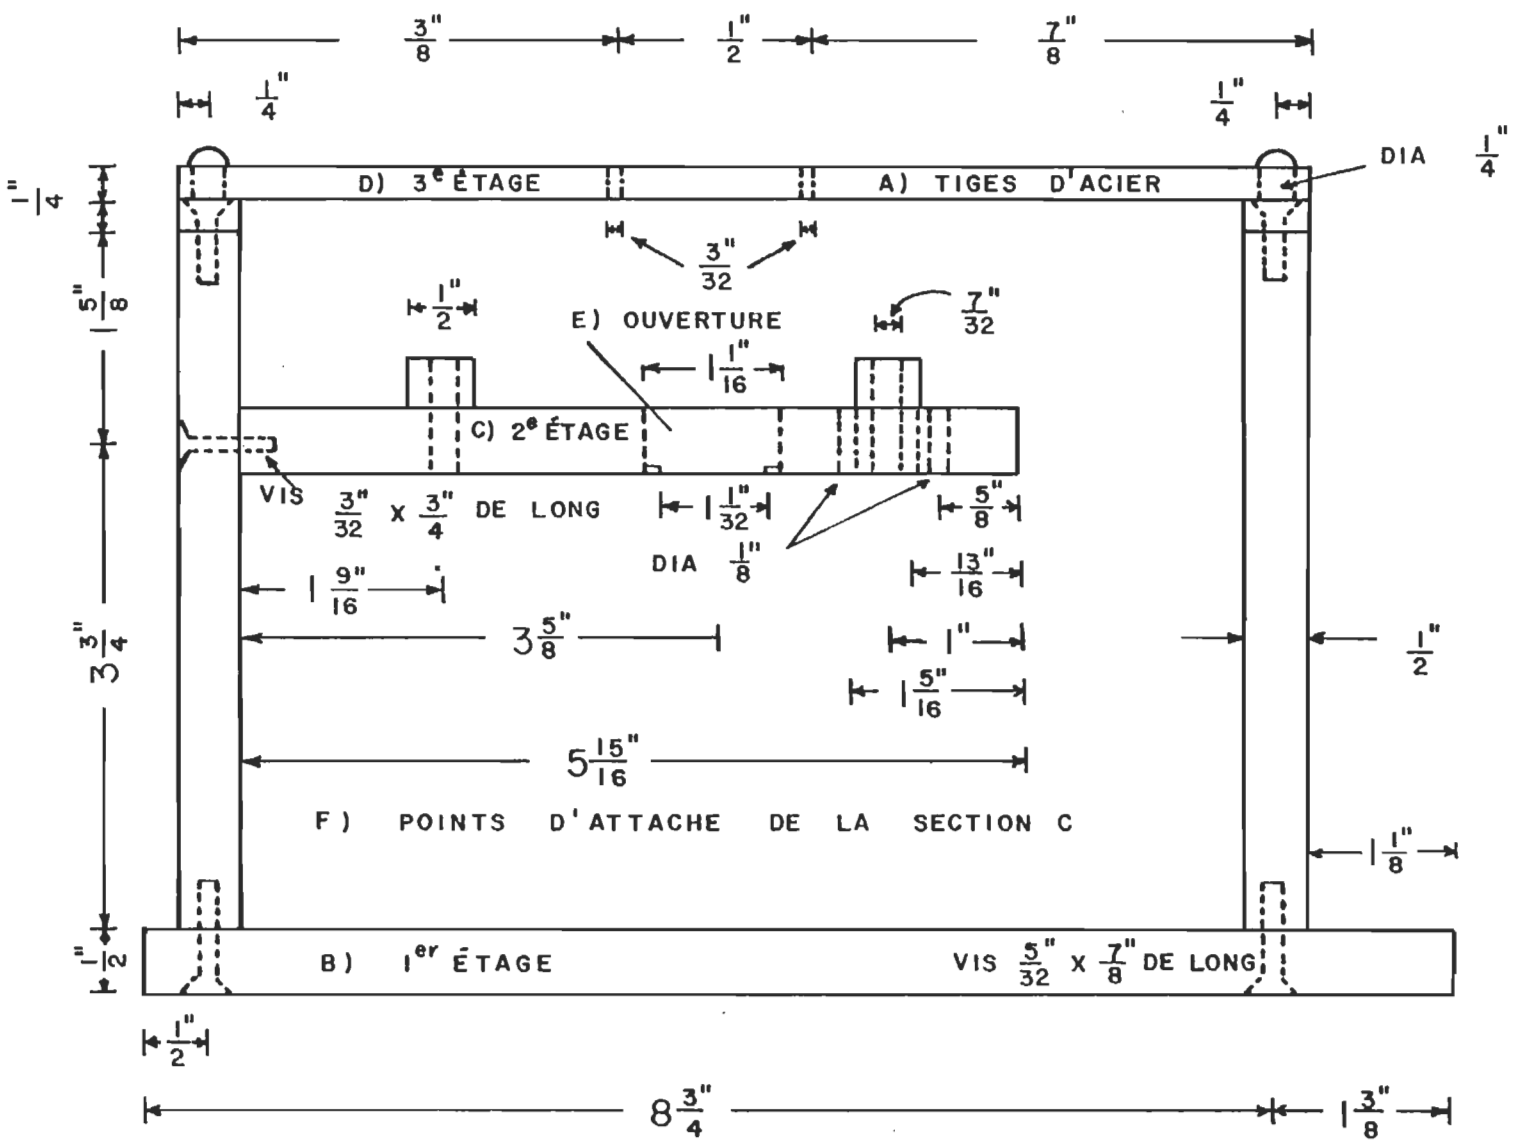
Plan détaillé de la section d vue dans le plan vertical gauche.
